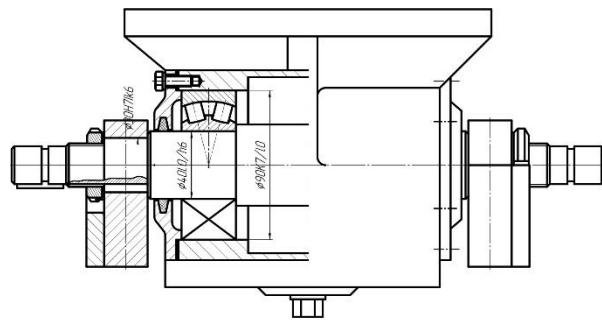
Переріз підшипникового вузла дебалансного вала вібротумби.
